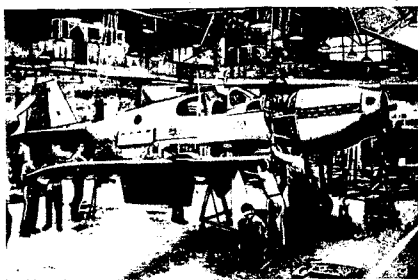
Приспособления для сборки боковых панелей фюзеляжа
